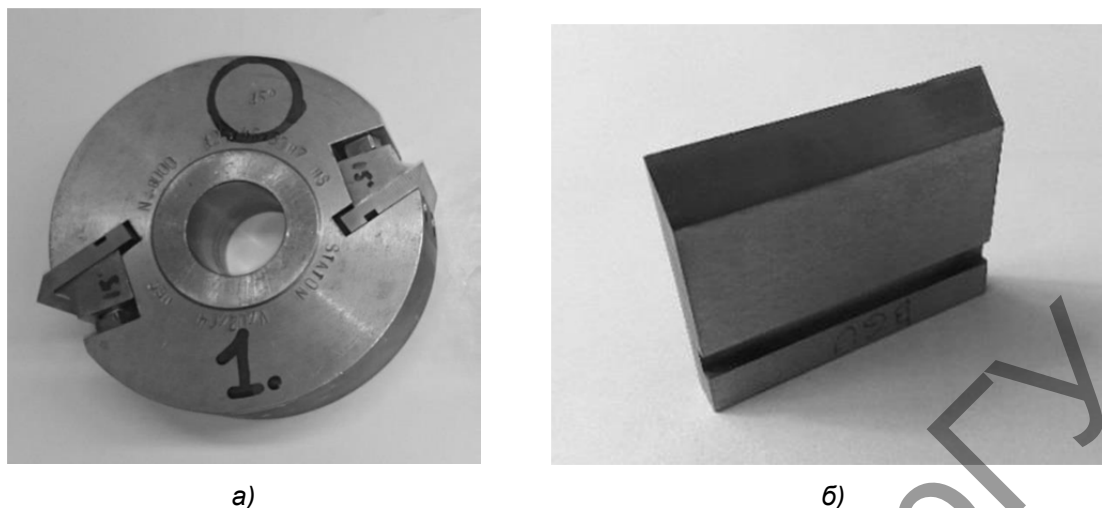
Фрезерная головка (передний угол — 15°) (а) и сменный нож фрезы (б)
